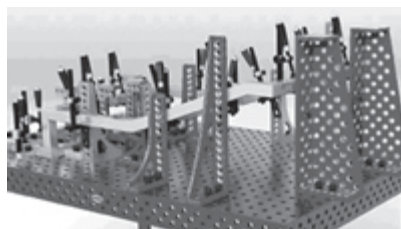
Многофункциональный сборно-разборный сварочный стапель
